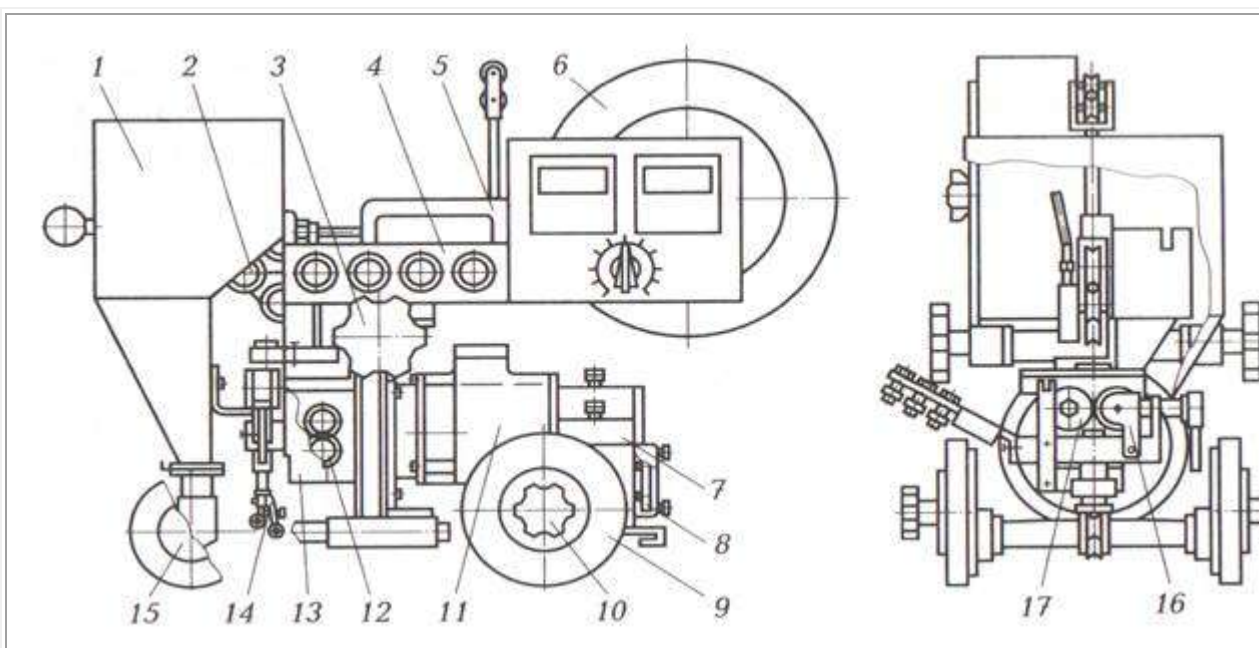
Сварочный трактор ТС-17
